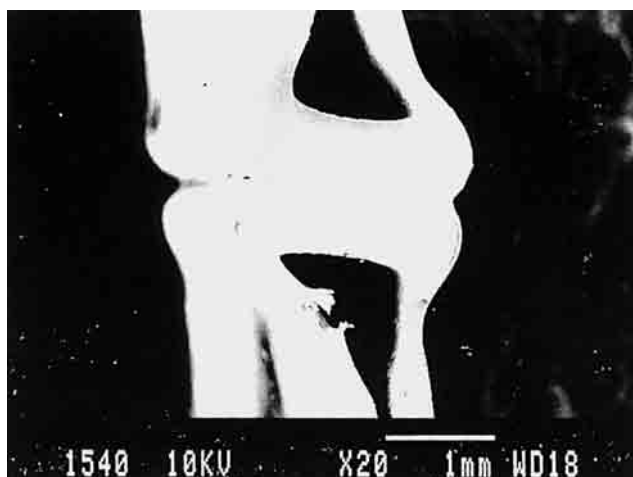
Место разрыва деформируемой заготовки наполнителя в образце № 1
